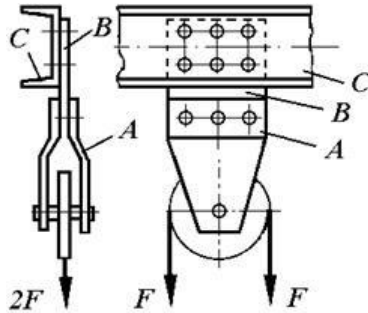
Заклепувальні з'єднання косинки зі швелером
